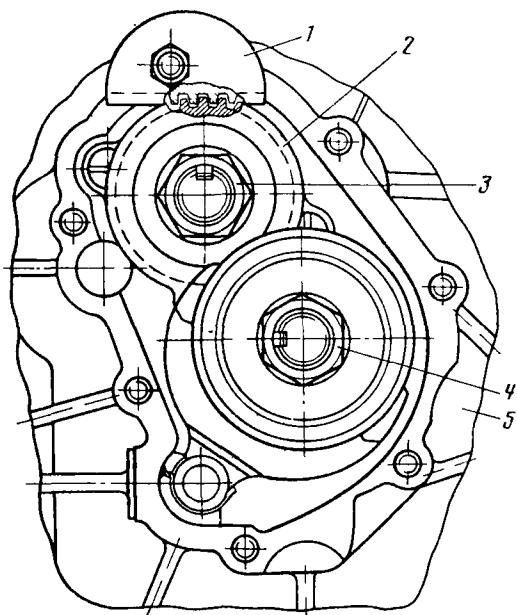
Стопорение V передачи коробки передач при отворачивании и заворачивании гаек ведущего и ведомого валов:
